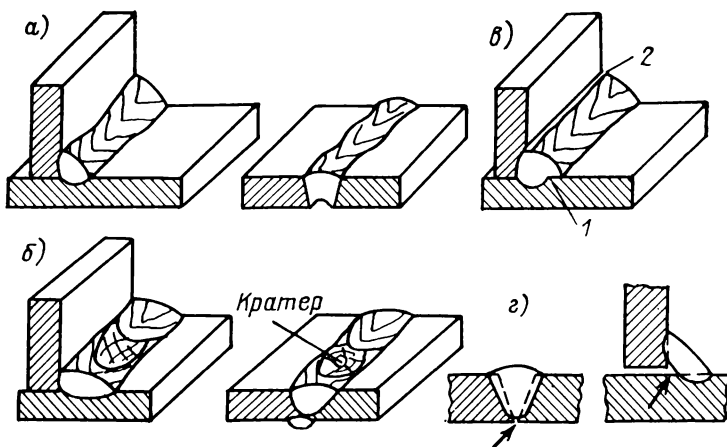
Наружные дефекты сварных соединений: а — неравномерность сечения швов по длине, вогнутость корня шва; б — кратеры с усачной раковинной, смещение продольной оси швов от заданного положения; в — наплывы 1 и подрезы 2; г — непровары.
